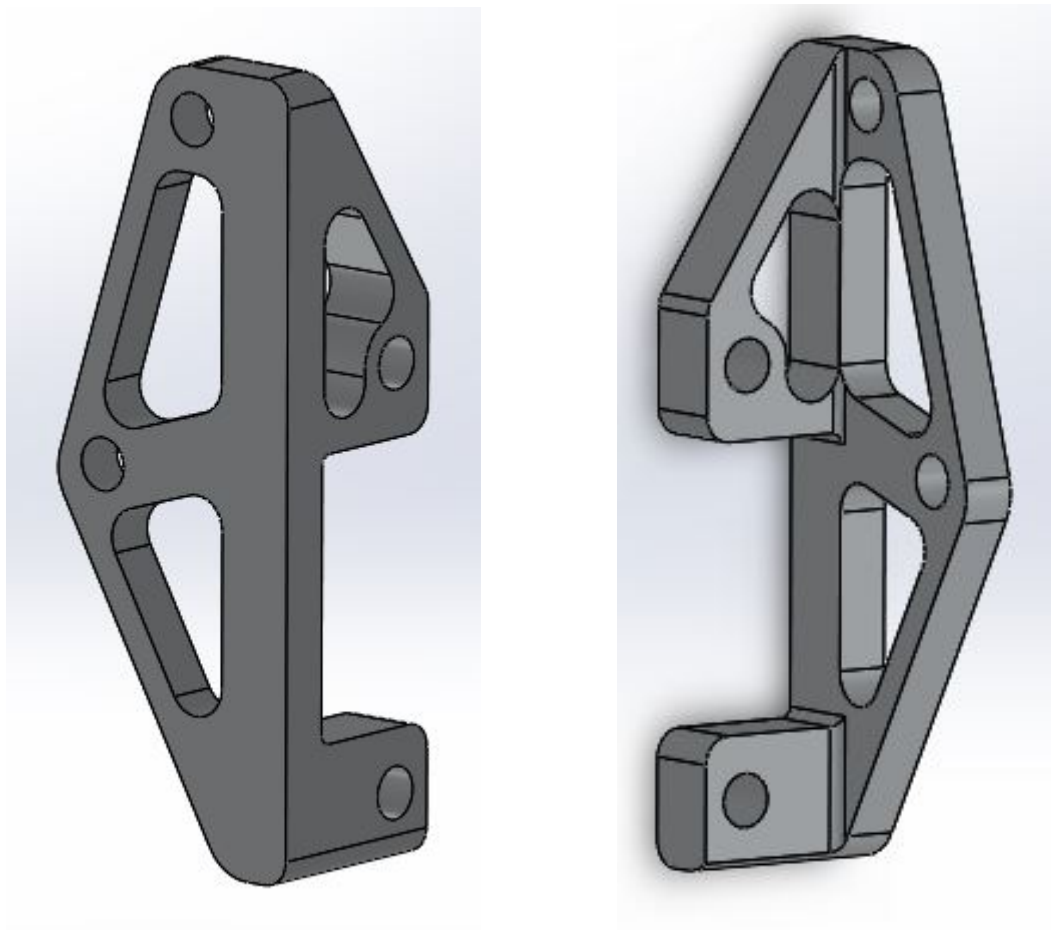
Diseño definitivo. Vista isométrica delantera y trasera.
